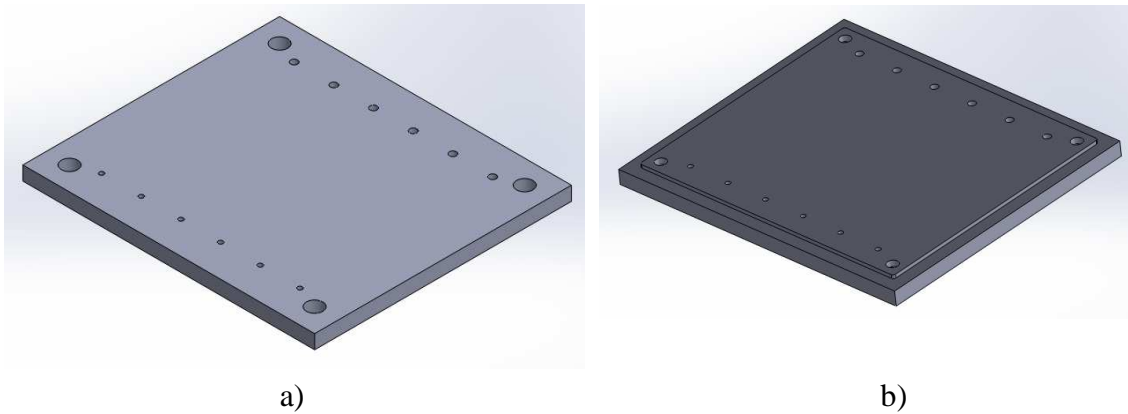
Placa superior do molde: a) Superfície exterior, b) Superfície interior.
